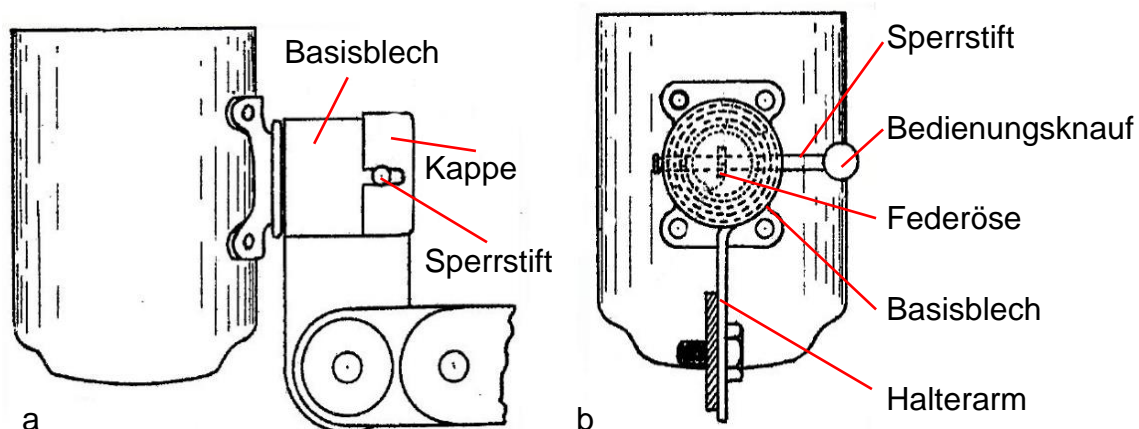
Kippvorrichtung am Gehäusemantel: a) Seitenansicht, b) Stirnansicht
